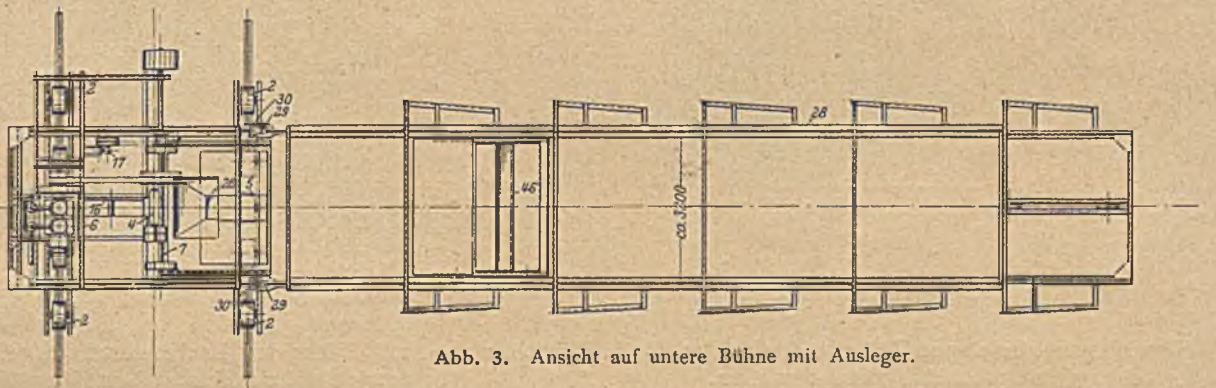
Ansicht auf untere Bühne mit Ausleger.
